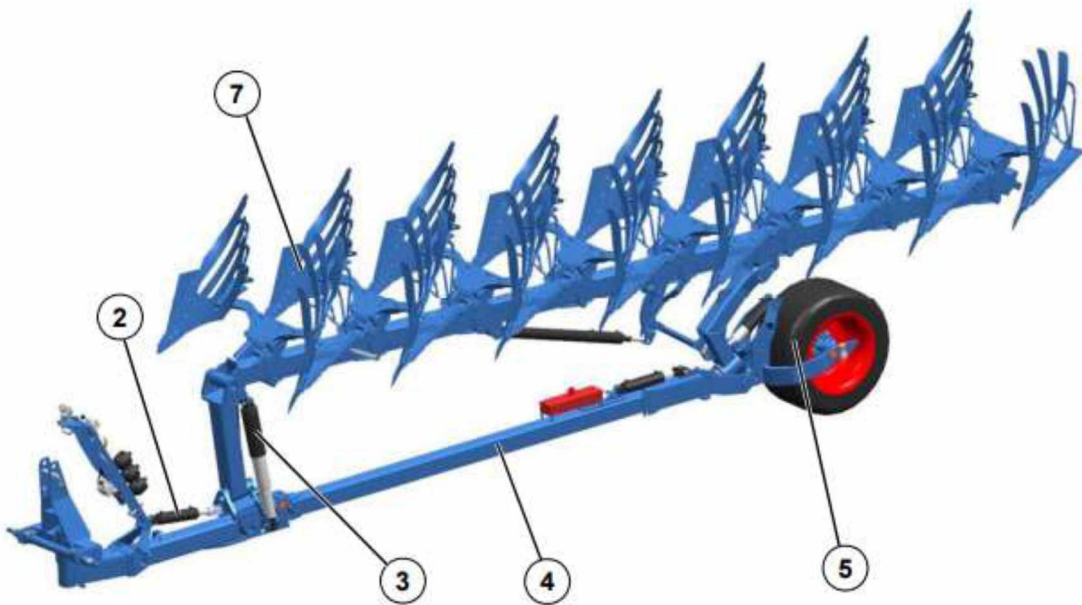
Загальний вид оборотного плуга фірми «Лемкен»
